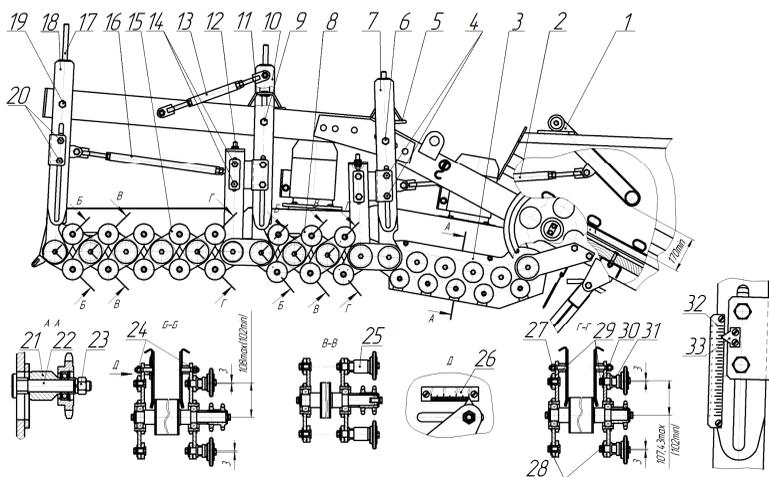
Схема регулировки углов наклона и зазора между валками калибратора и ворохоочистителя ПКСП-25:
